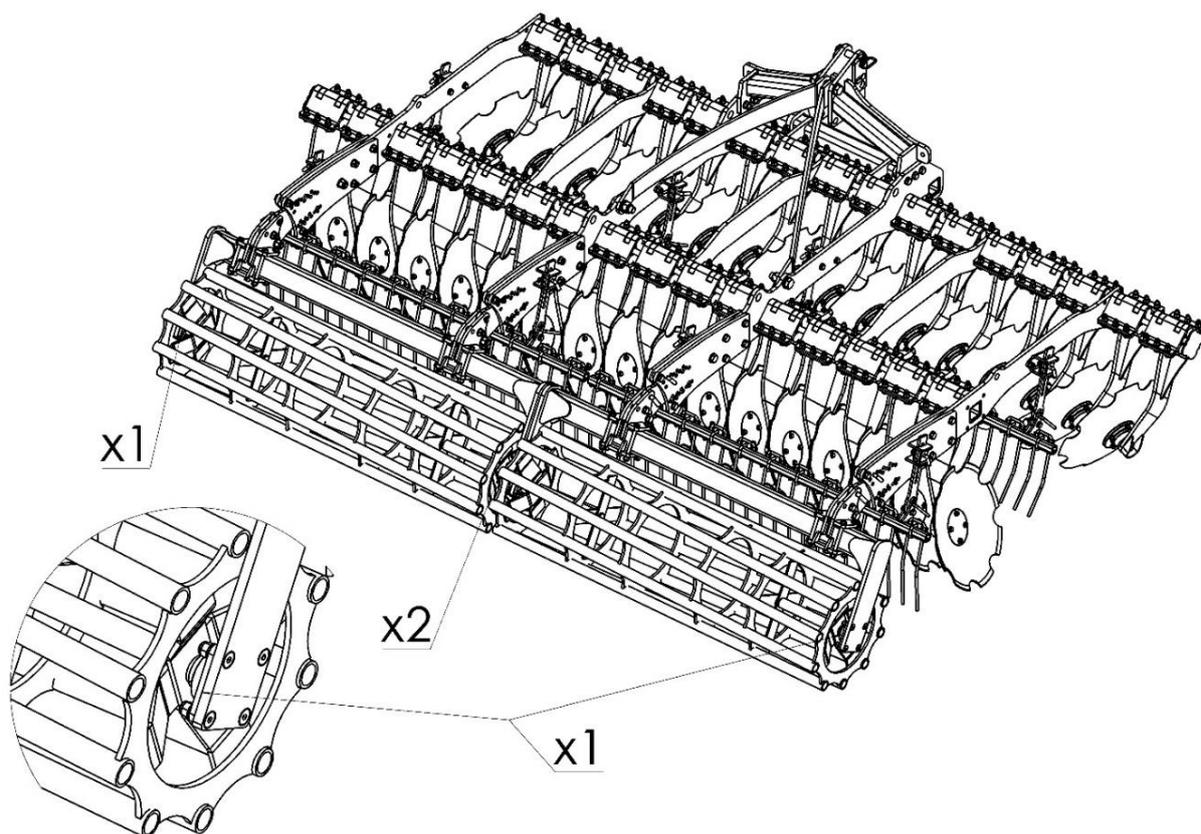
Узел подшипника вала – 4 точки смазки (версия 4 м), 2 точки смазки (версии 3,5 м, 3 м)
